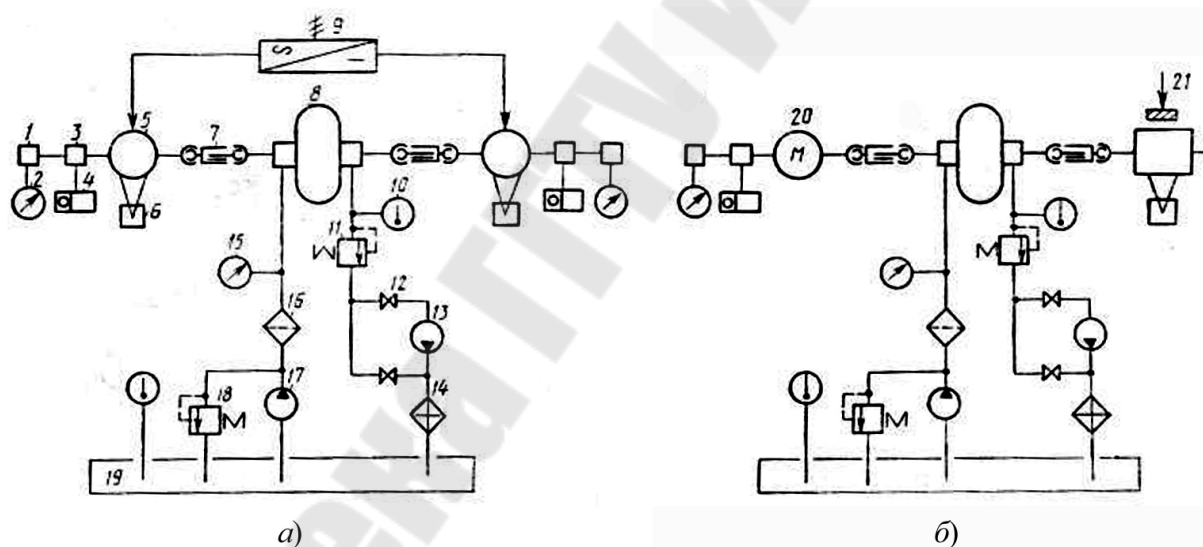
Схемы стендов для испытания гидродинамических передач:
